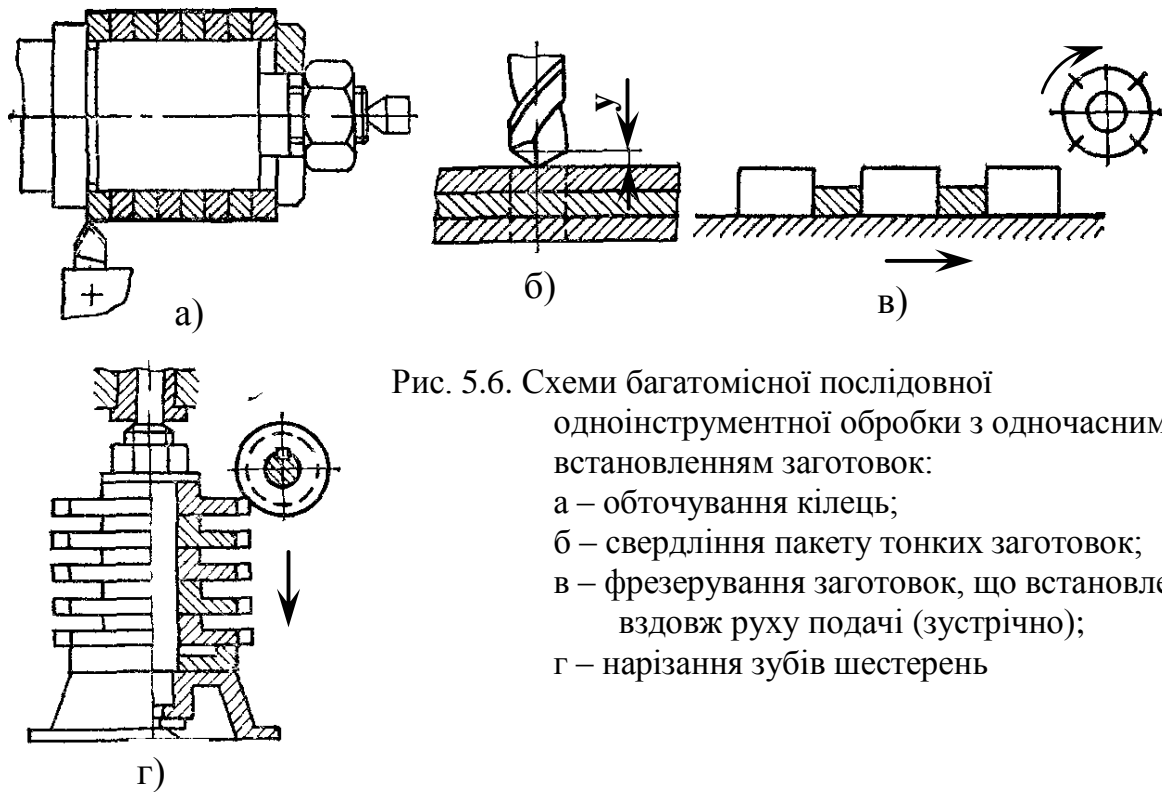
Схеми багатомісної послідовної одноінструментної обробки з одночасним встановленням заготовок:
